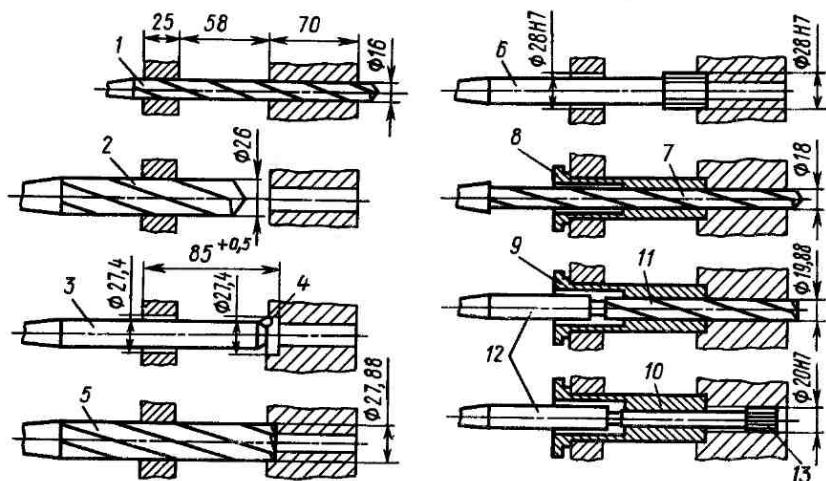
Обработка отверстий $\varnothing 20H7$, $28H7$
